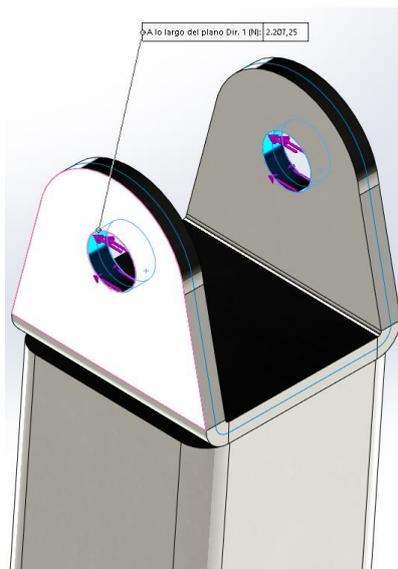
Detalle fuerza 2 del conjunto de palanca con extras.
